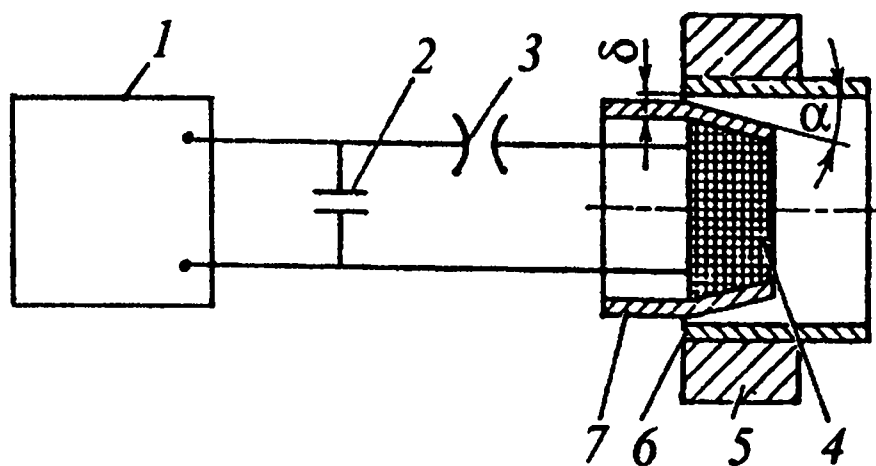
Схема магнитоимпульсной сварки
